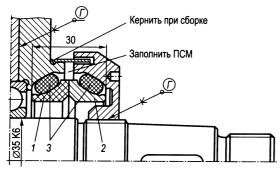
Торцовое уплотнение вала редуктора, используемого в строительстве: 1 — неподвижное кольцо из углеграфита 2П-1000Ф; 2 — вращающееся кольцо из стали 95X18 (55HRC₃); 3 — уплотнительные резиновые кольца круглого сечения 050-060-58 по ГОСТ 9833—73 (для их деформирования осевое перемещение гайки составляет 3...4 мм)
